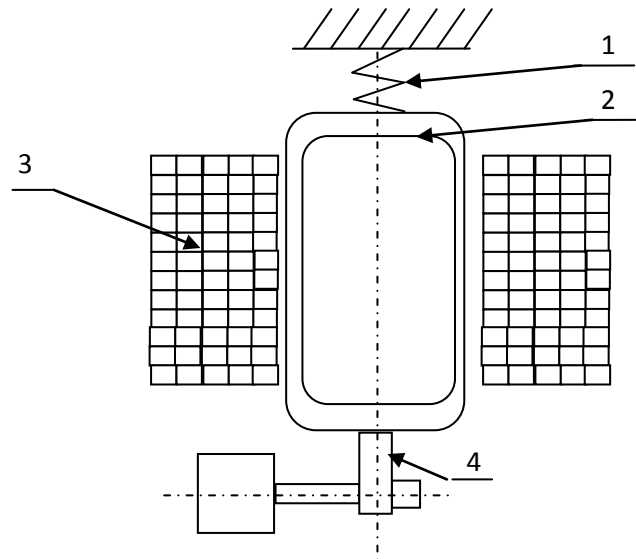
Схема установки вібромагнітноабразивного оброблення (ВіМАО): 1 – пружні опори; 2 – робоча камера, яка виготовлена з SiCa; 3 – статор; 4 – ексцентрик
